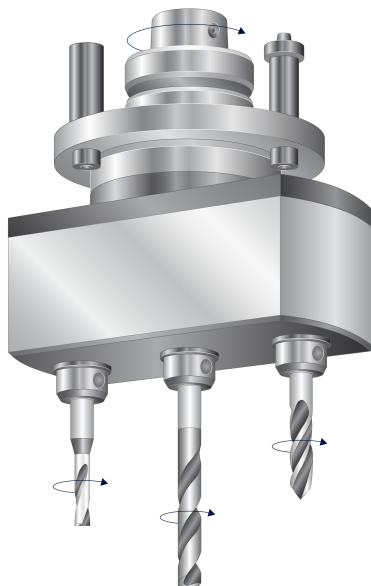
Werkzeugsystem mit mehreren Bohrern
